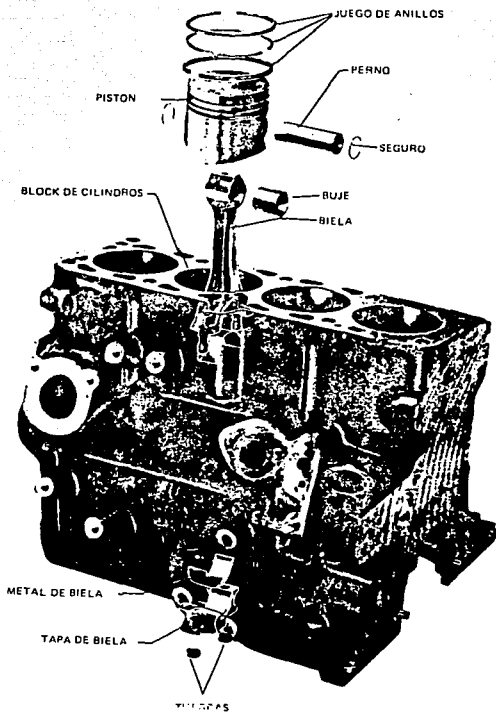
Bloque de cilindros. Motor Caribe VW 1600.
